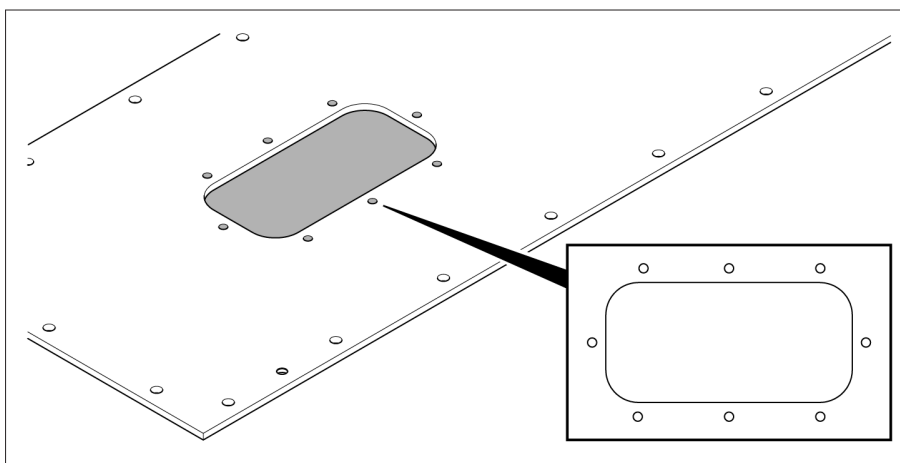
Верхняя сторона крышки трансформатора с отверстием для соединительного модуля с уплотнением
